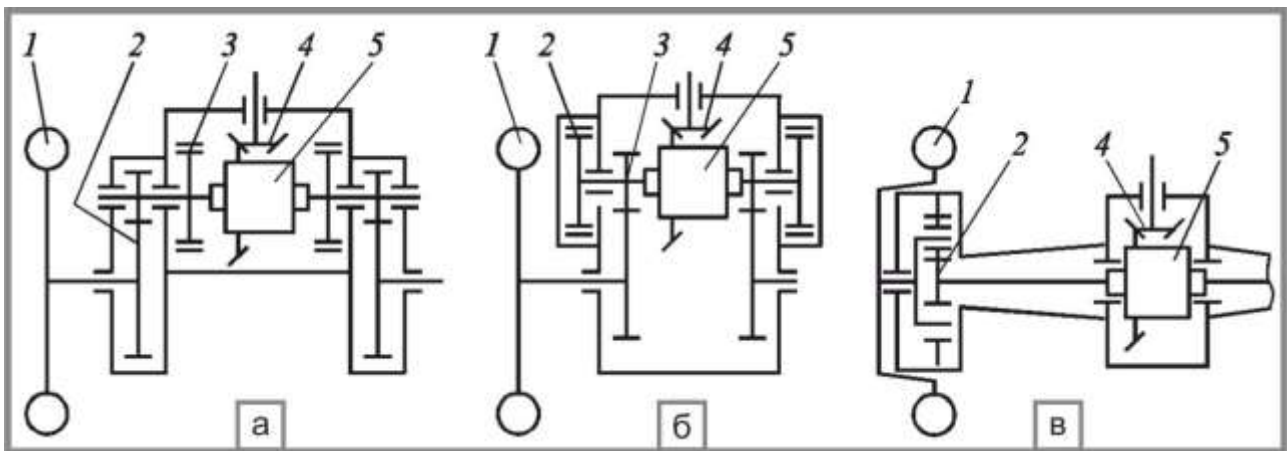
Кінематичні схеми задніх ведучих мостів автомобілів: а – в окремому корпусі; б – у корпусі заднього моста; в – з планетарним редуктором у колесі; 1 – ведуче колесо; 2 – кінцева передача; 3 – гальмо; 4 – головна передача; 5 – міжколiсний диференціал
